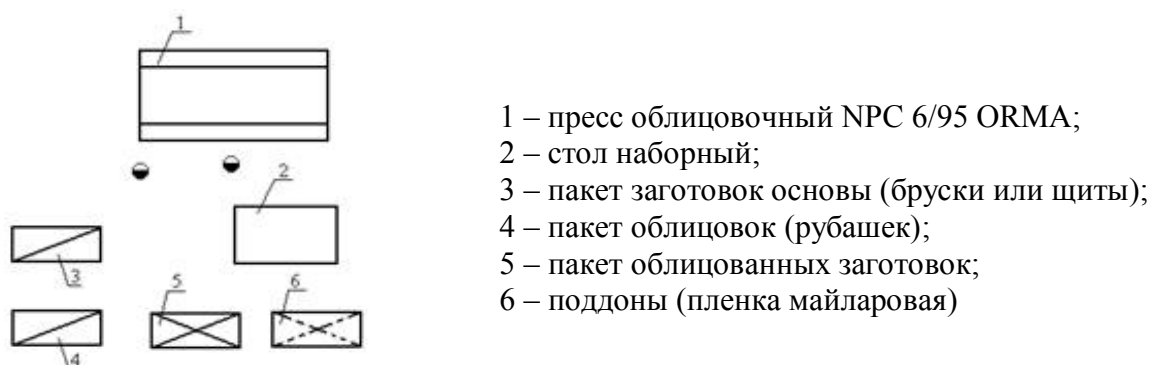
План рабочего места у одноэтажного пресса для облицовывания пластей
